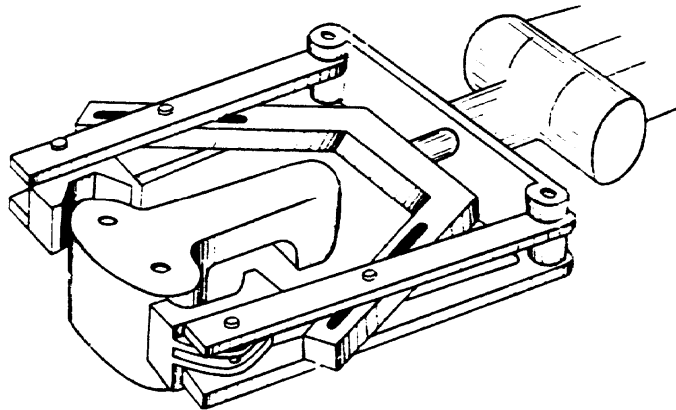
Захоплювач для роботи з важкими і громіздкими деталями
